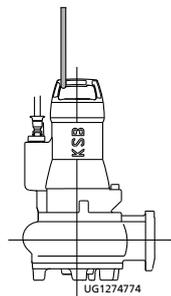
Halterung montieren bei 2-Stangenführung
